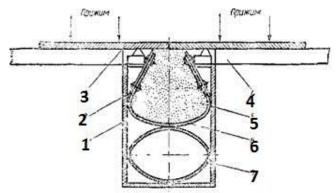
Схема приспособления для сварки на флюсовой подушке: 1 — корыто; 2 — упорная планка; 3 — свариваемый лист; 4 — сварочный стол; 5 — флюсовая подушка; 6 — брезентовая ткань; 7 — шланг (изображен в рабочем положении). [8].
